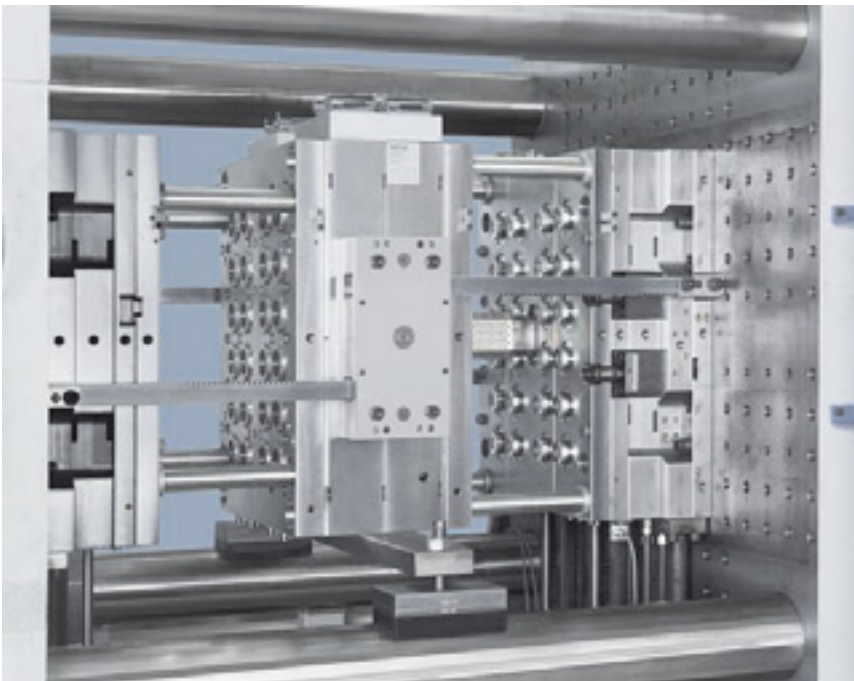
24+24-fach Becherwerkzeug mit Zahnstangenantrieb [13.13]
